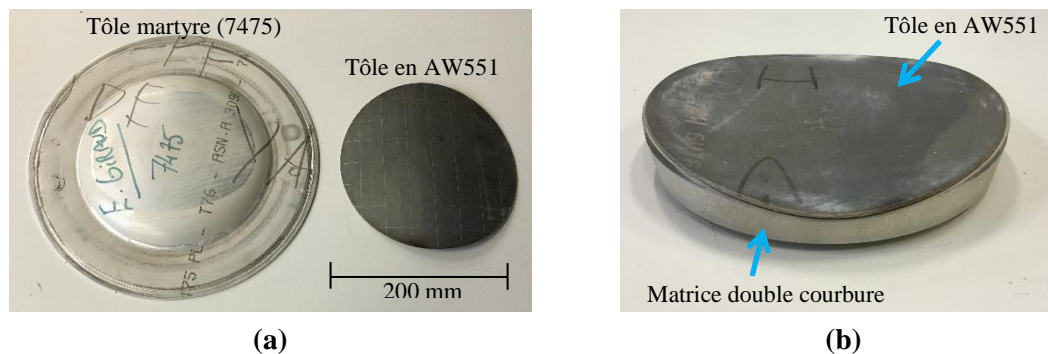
Pièces obtenues après la mise en forme par fluage avec la machine de gonflage
